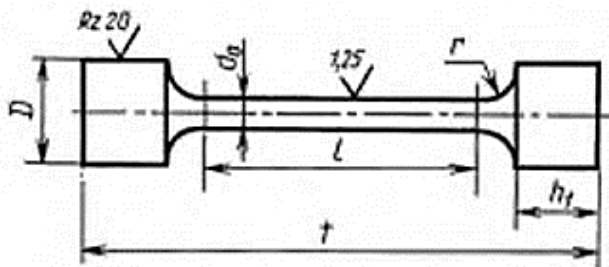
Форма образца из цельной или сварной заготовки
